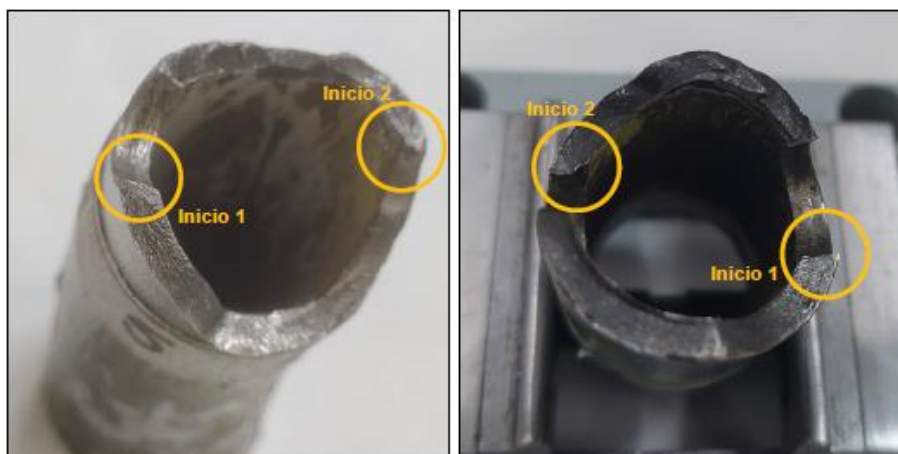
1) Inicios de fractura, tramo A, 25X. 2) Inicios de fractura, tramo B, 25X. Fuente: investigación JST
